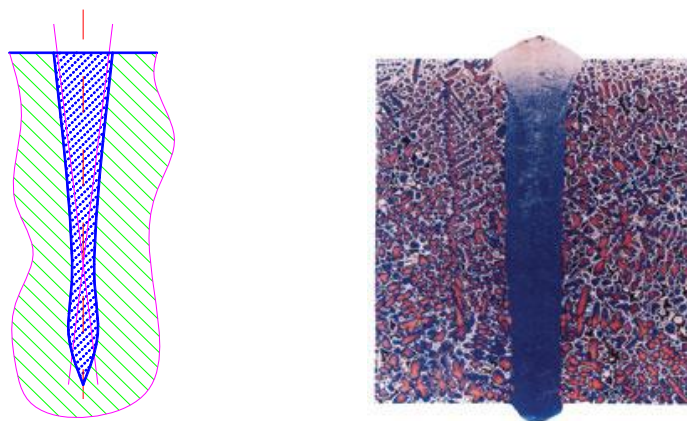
Вигляд «кинджального» проплавлення зварного шва
